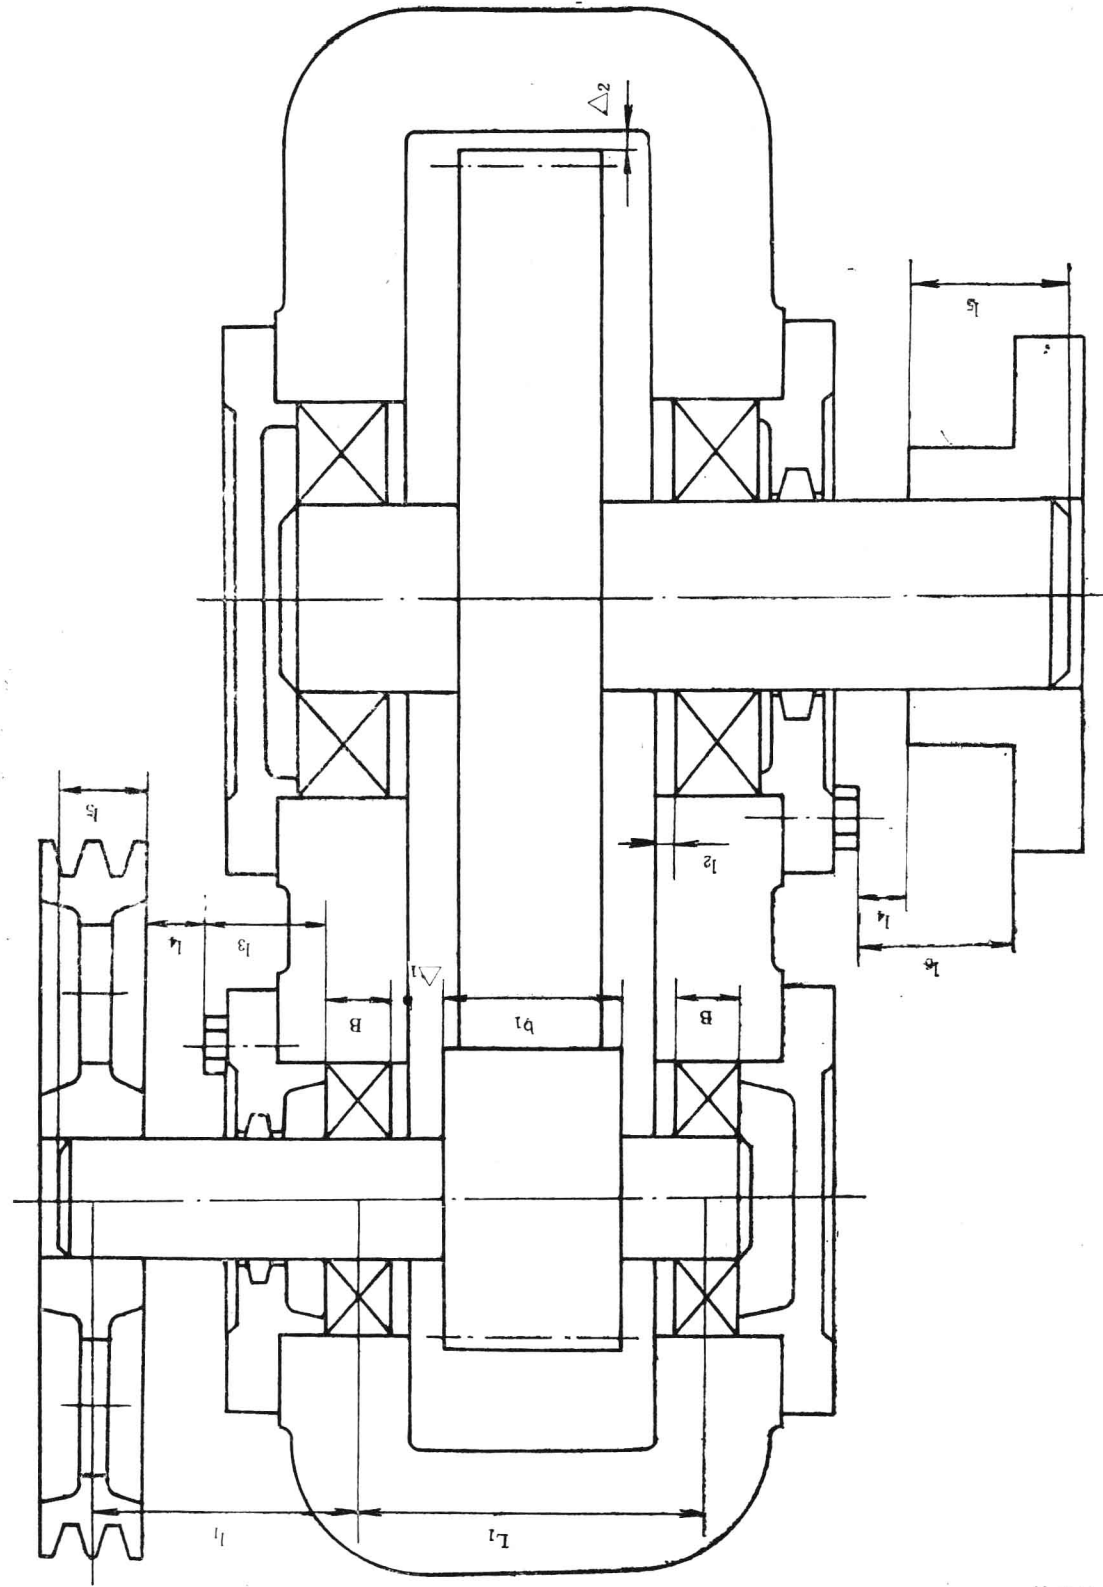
单级圆柱齿轮减速器零件的位置尺寸
